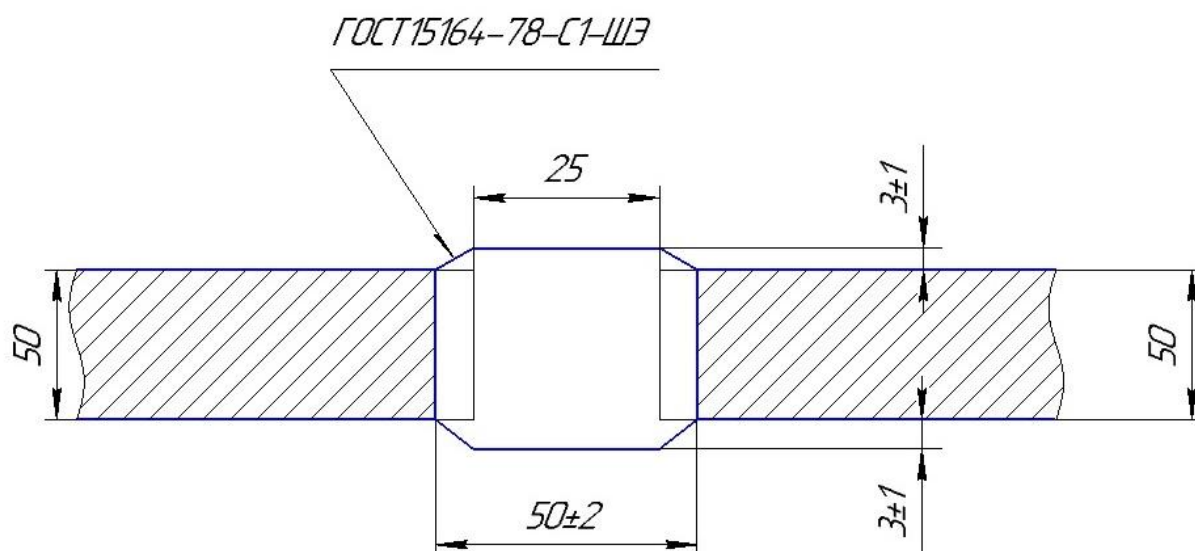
Сварной шов С1 – ЭШС
